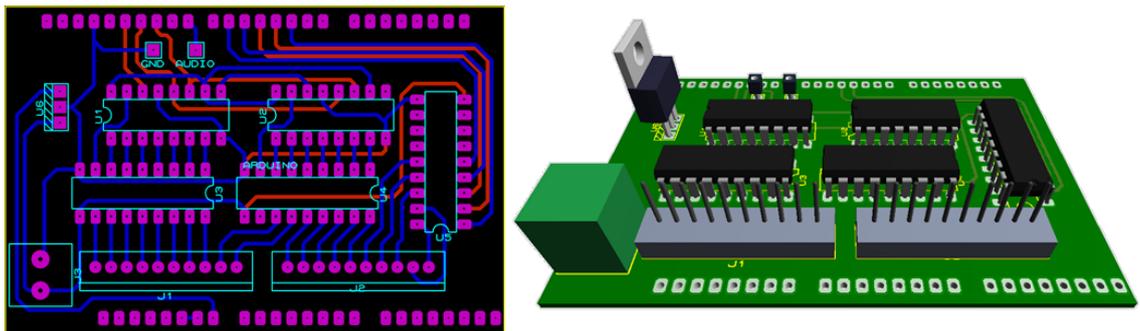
Diseño de la PCB del Módulo de Motricidad
